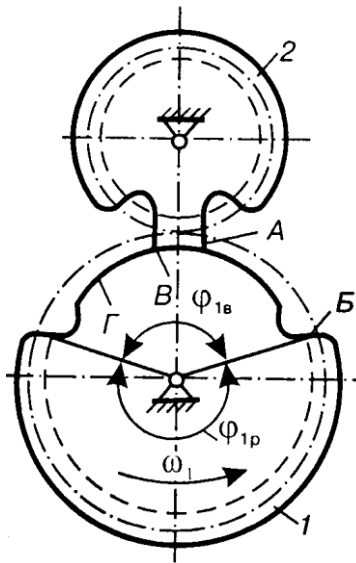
Схема механізму переривчастого руху з неповнозубими колесами
